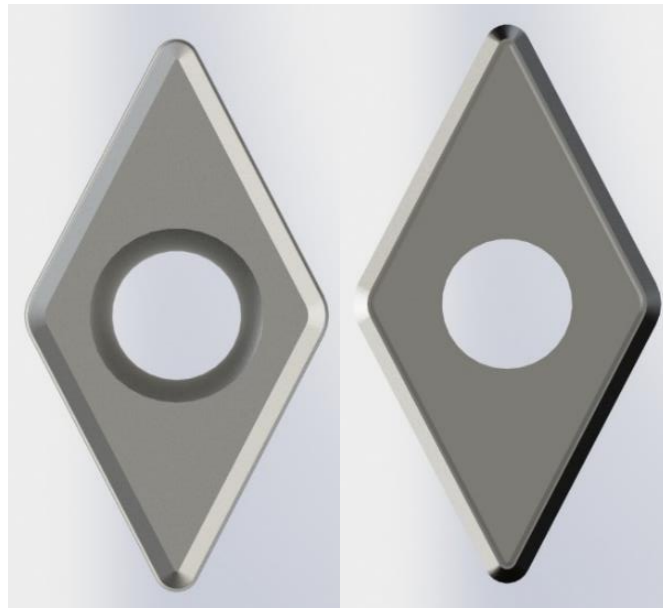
Plaquita modelada en vista alzado y perfil respectivamente.
